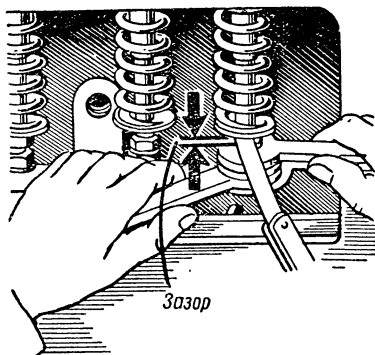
Регулировка зазора между толкателем и стержнем клапана
